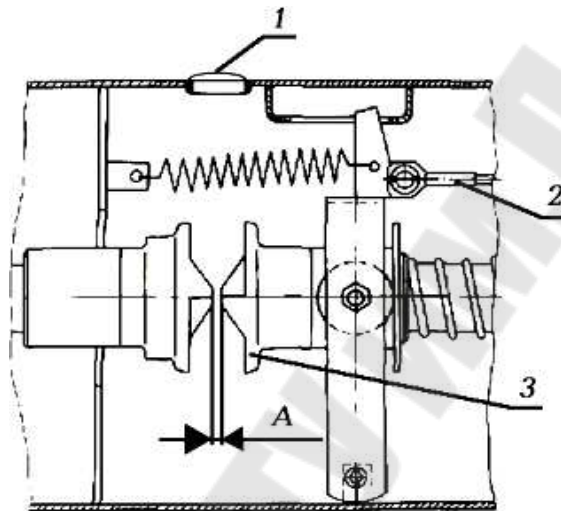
Схема регулировки кулачковой муфты привода: 1 – крышка; 2 – трос; 3 – полумуфта
